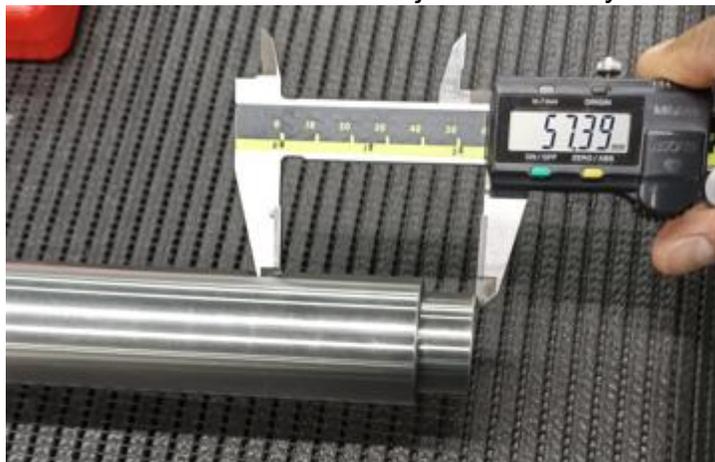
Ejemplo de inspección de dimensiones a producto terminado.
